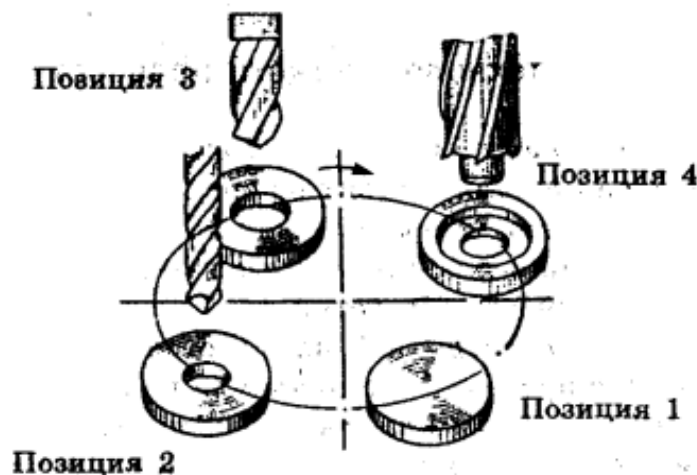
Обработка детали на сверлильном станке: позиция 1 – установка заготовки; позиция 2 – сверление; позиция 3 – зенкерование; позиция 4 – развёртывание
